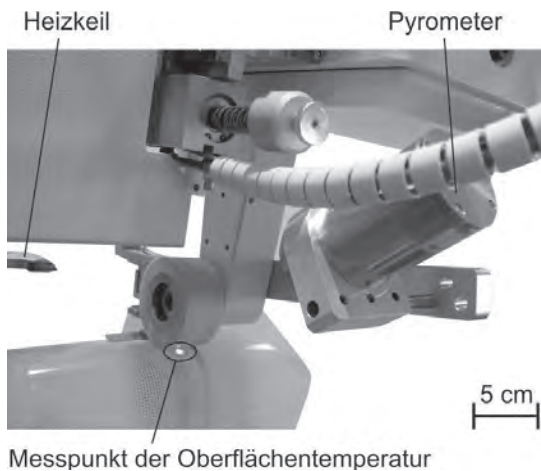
Befestigtes Pyrometer an Heizkeilschweißmaschine
